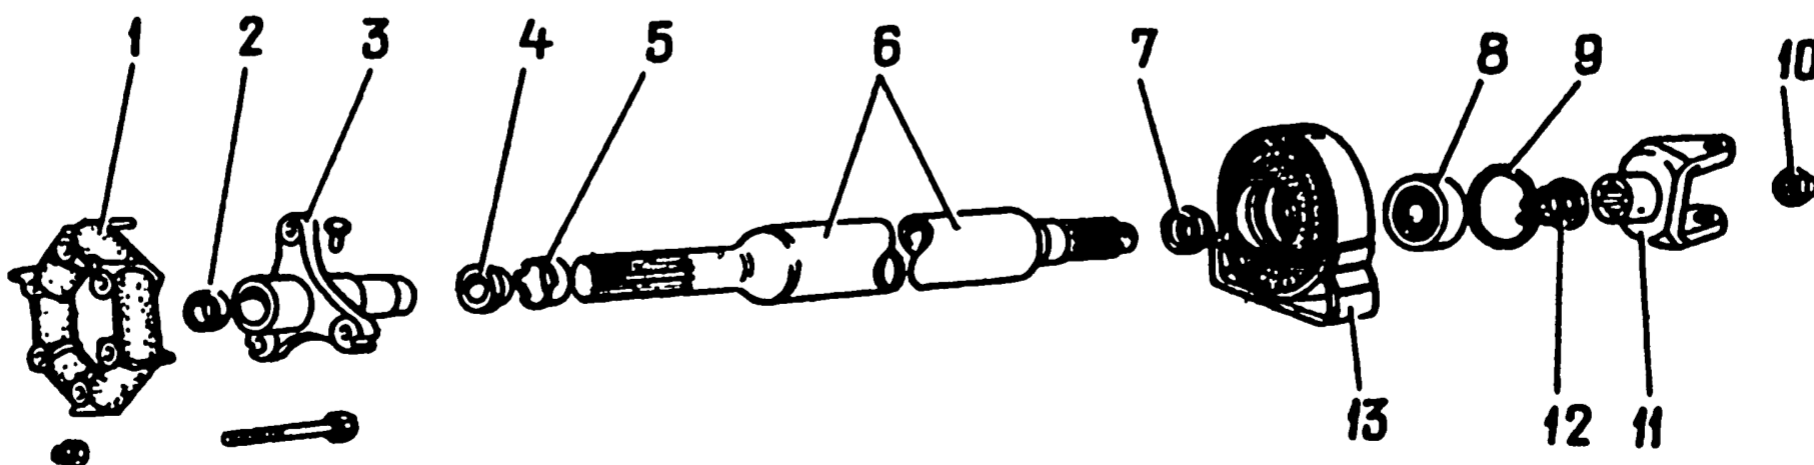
Детали переднего карданного вала: 1 - эластичная муфта; 2 - центрирующая втулка; 3 - фланец эластичной муфты; 4 - сальник; 5 - обойма сальника; 6 - карданный вал; 7 - пылеотражатель; 8 - подшипник; 9 - стопорное кольцо; 10 - гайка; 11 - вилка карданного шарнира; 12 - пылеотражатель; 13 - упругая опора
